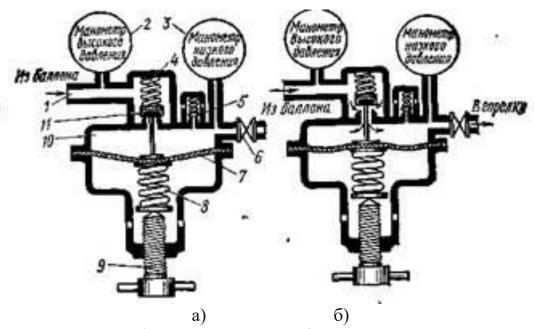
Схема устройства и работы газового редуктора а — нерабочее положение (газ не идет через редуктор), б — рабочее положение (газ проходит через редуктор).
